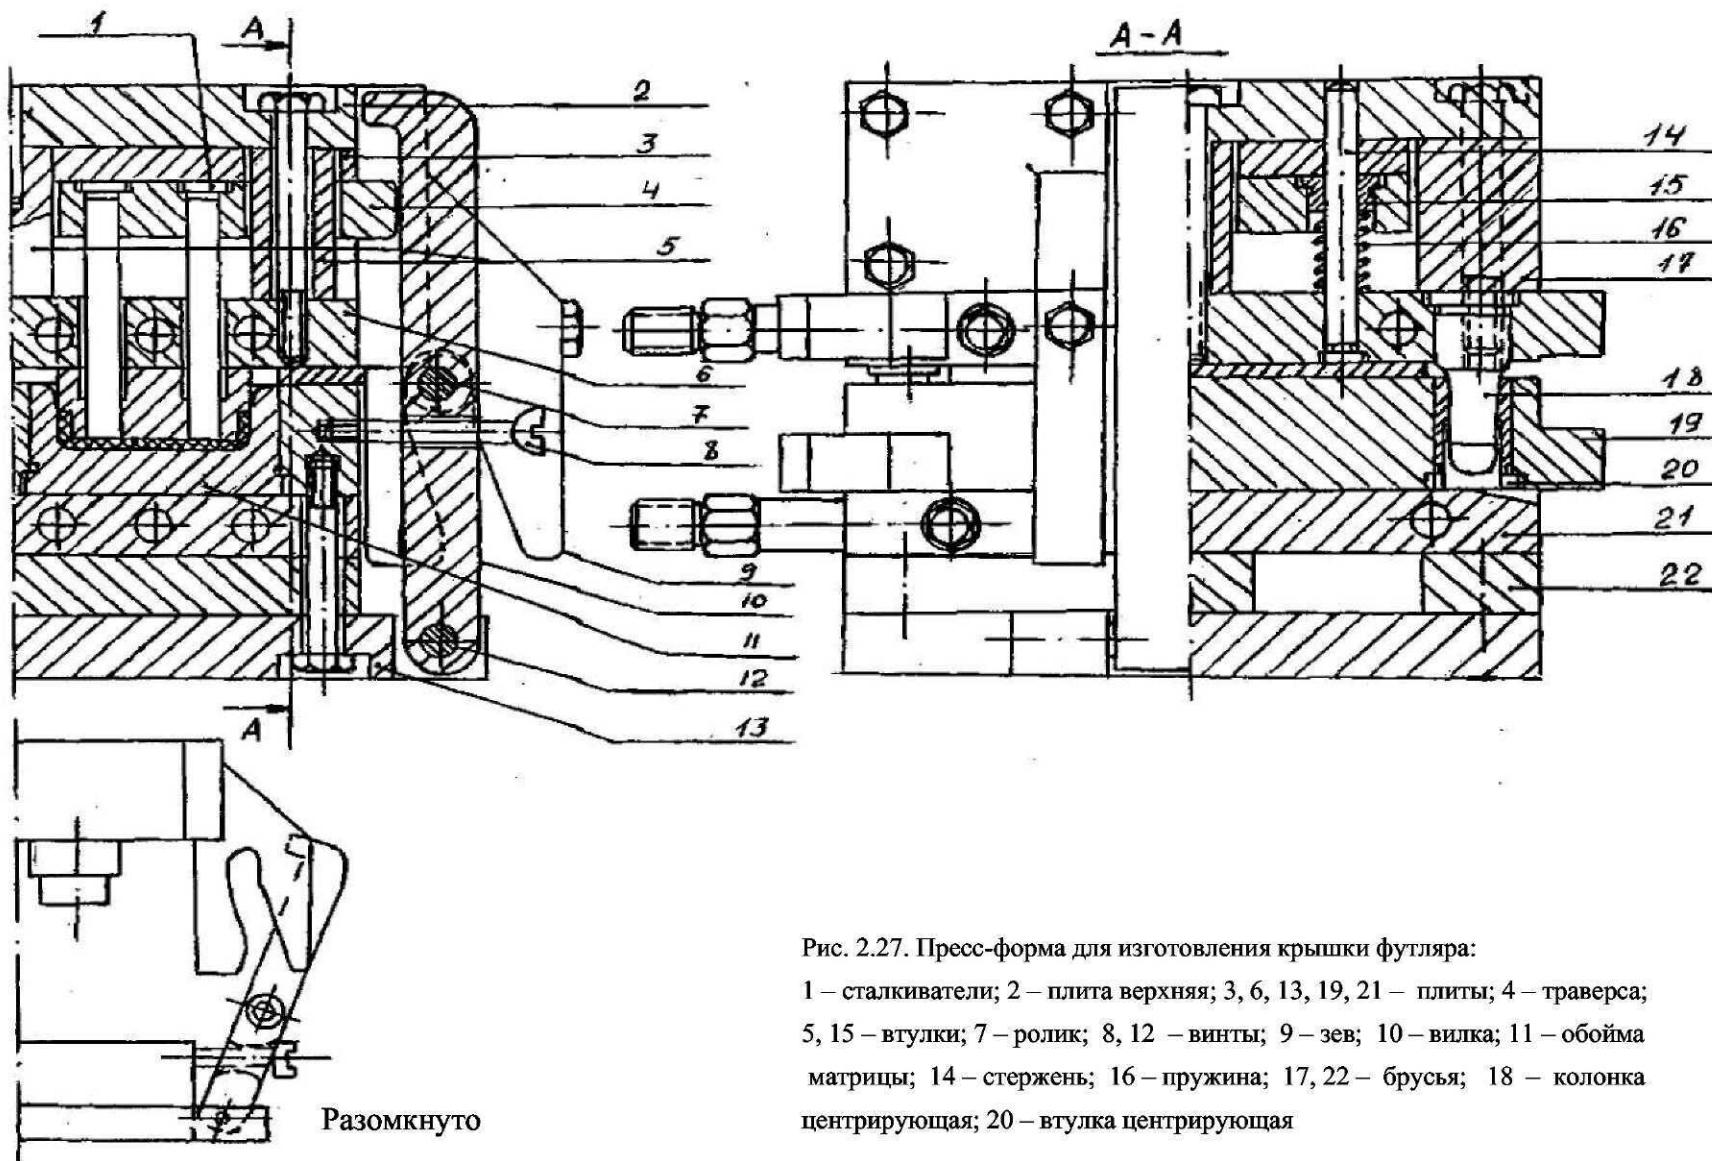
Пресс-форма для изготовления крышки футляра:
